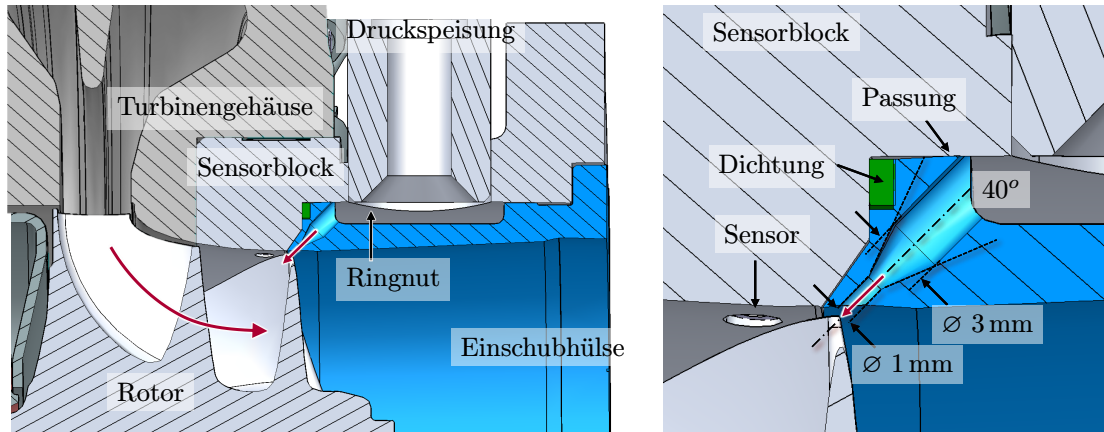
Detaildarstellung des Basisdesigns der Düseninblasung am Turbinenaustritt
